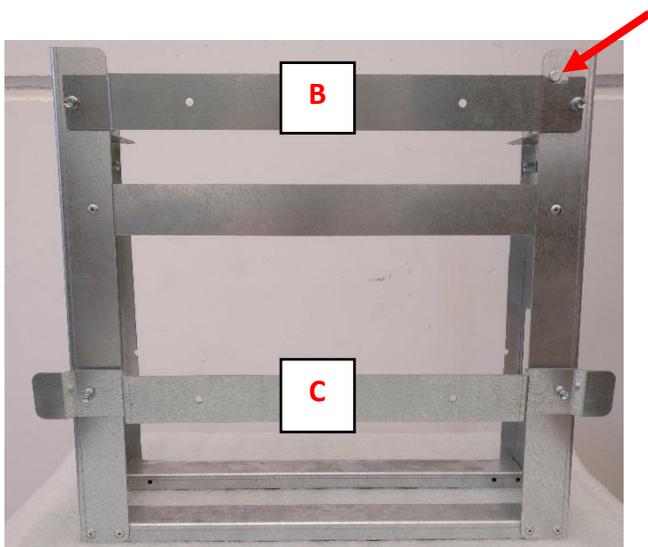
Instalación de las abrazaderas en la caja de baterías
